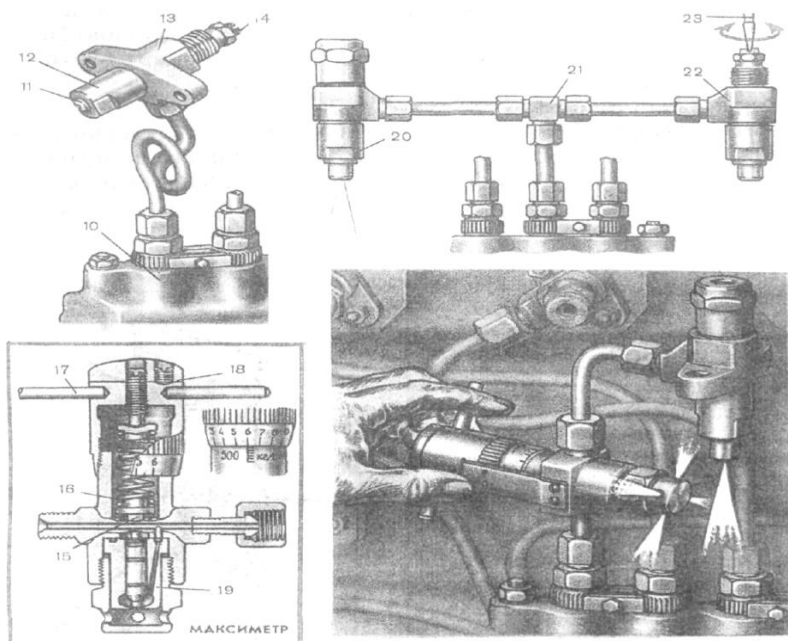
Перевірка роботи форсунки максиметром і контрольною форсункою: 10 – корпус паливного насоса; 11 – штифтовий розпилювач; 12 – гайка розпилювача; 13 – корпус форсунки
